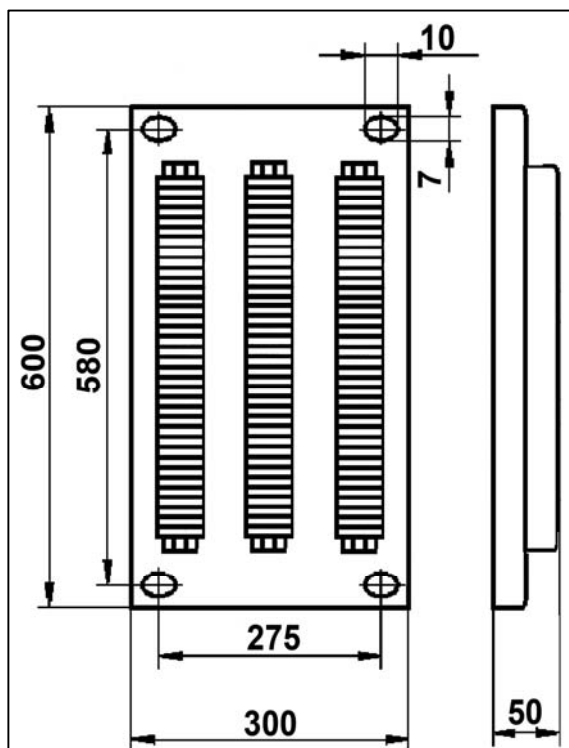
Габаритные и установочные размеры блока БК-3-У3
